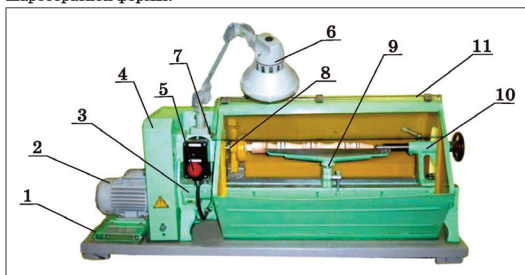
Токарный станок по обработке древесины: 1 – основание; 2 – электродвигатель; 3 – станина; 4 – ограждение ременной передачи; 5 – магнитный пускатель; 6 – светильник; 7 – передняя бабка; 8 – шпиндель; 9 – подручник; 10 – задняя бабка; 11 – защитный экран
